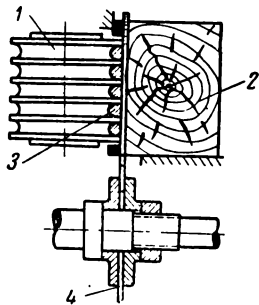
Схема станка для изготовления деревянных клиньев.
